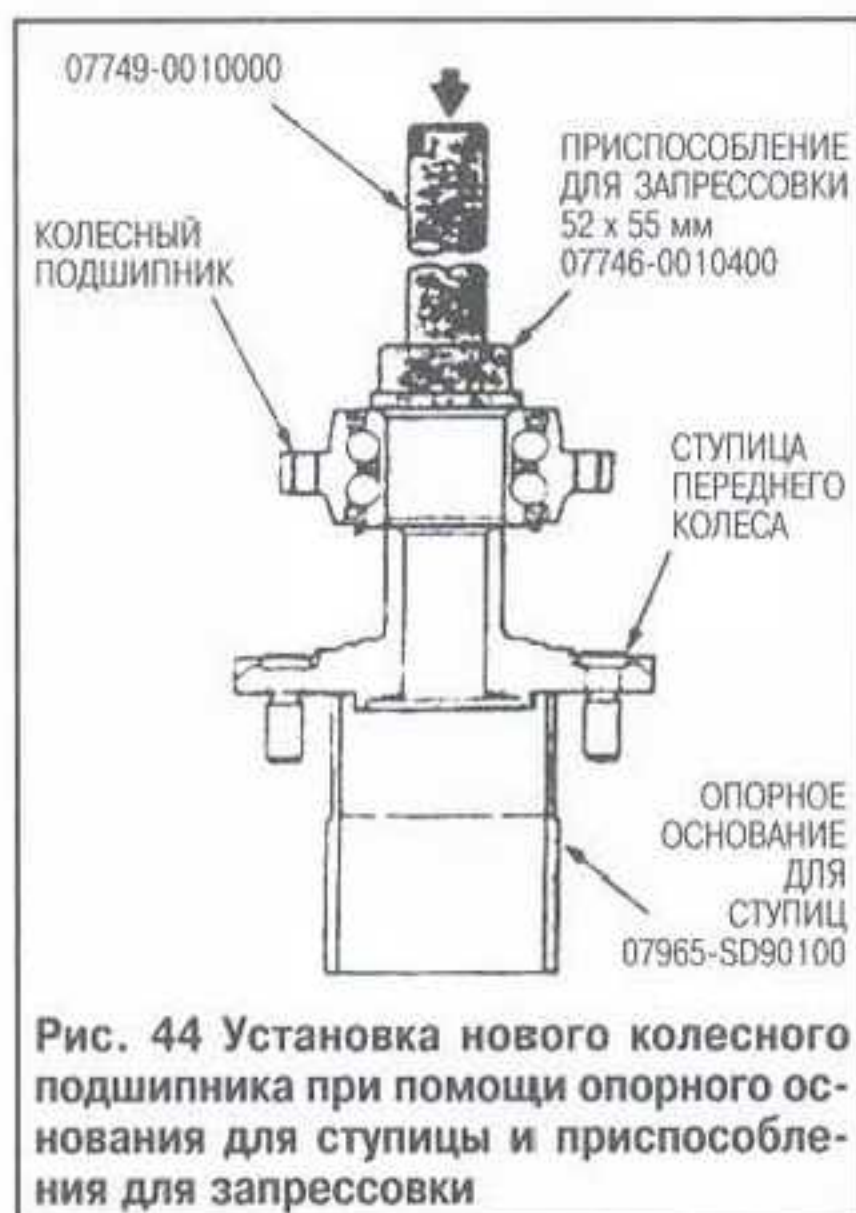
Установка нового колесного подшипника при помощи опорного основания для ступицы и приспособления для запрессовки
